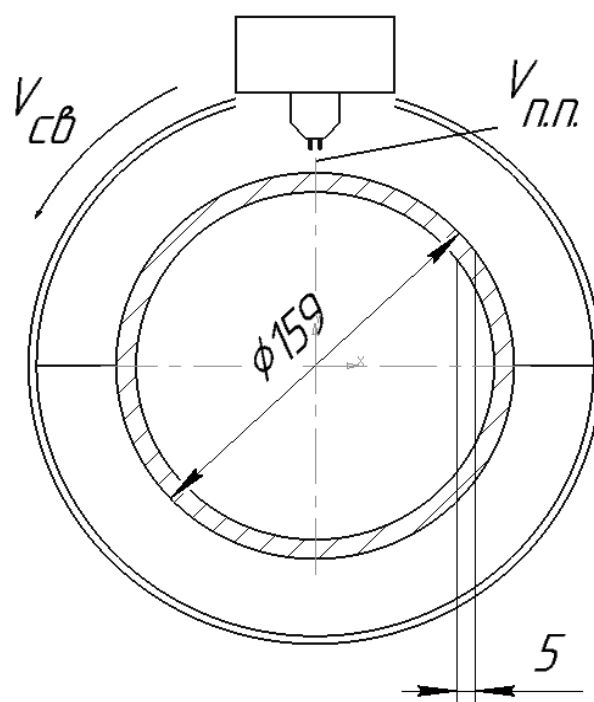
Схема сварки заполняющего шва
